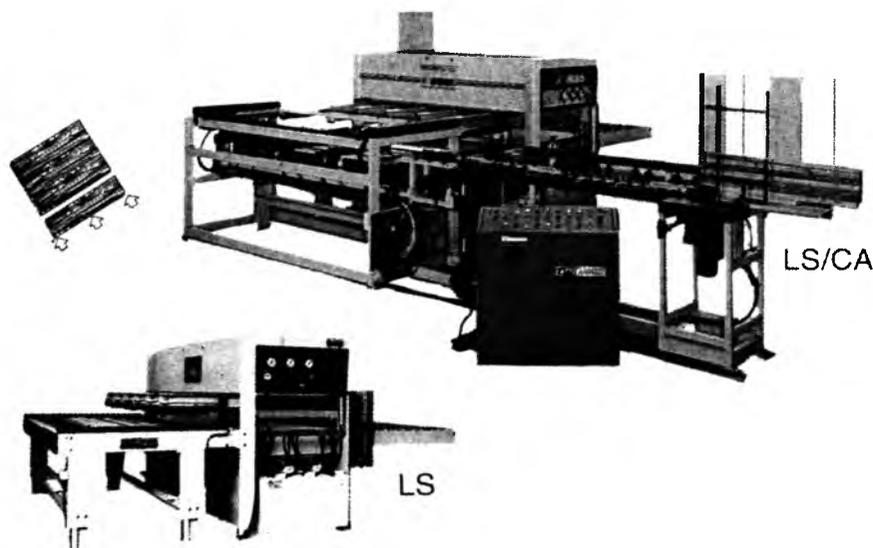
Прессы (LS/CA, LS) с вертикальным загрузочным устройством для горячего склеивания щитов из массивной древесины
